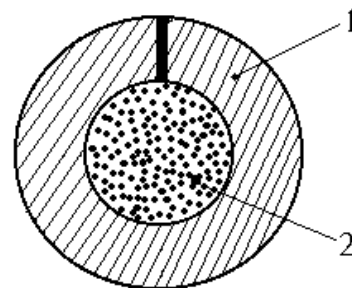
Конструкция порошковой проволоки: 1 – оболочка; 2 – порошкообразный сердечник
